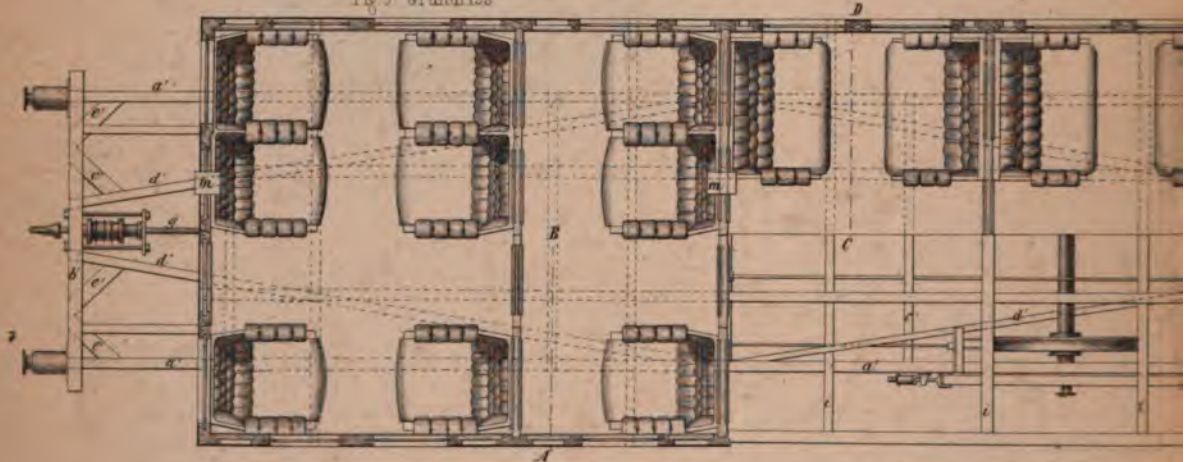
Grundriss d. 1. Cl. Wagen mit Cabinet.
